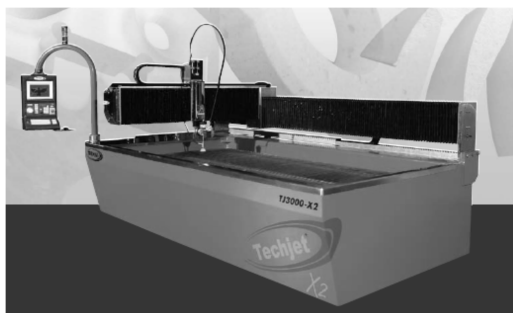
Типовая конструкция установки гидроабразивной резки с рабочей головкой, расположенной на консоли
